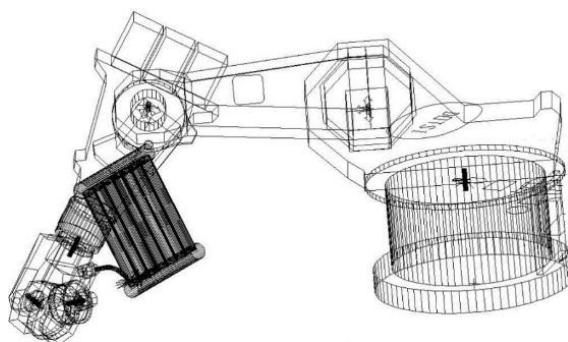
Роботизированная ячейка для дуговой сварки
